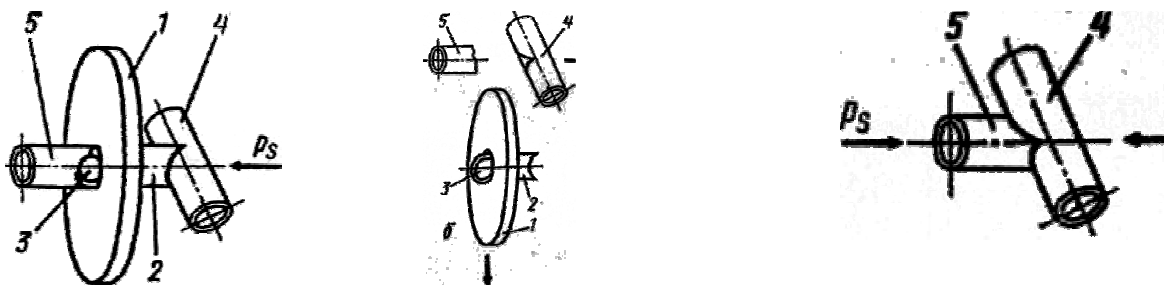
Принцип сварки разветвлений труб в выточку: а — подогрев свариваемых труб; б — отвод нагретого инструмента; в — состыковка (сварка); 1 — нагретый инструмент; 2 — сварочный инструмент для выравнивания кольцеобразной выточки в трубе большего размера; 3 — сварочный инструмент для разветвления трубы меньшего размера; 4 — труба большего размера; 5 — труба с условным проходом меньшего размера
